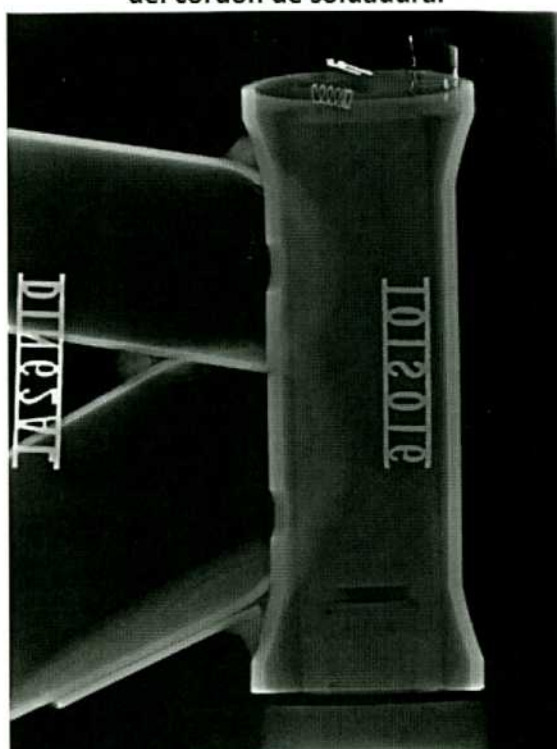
Radiografía de cuadro de Aluminio Vairo (tubo de dirección). Se observa el dispositivo de inspección por corrientes inducidas e indicaciones de posibles faltas de fusión en los distintos cordones de soldadura. Técnica: fluoroscopia
